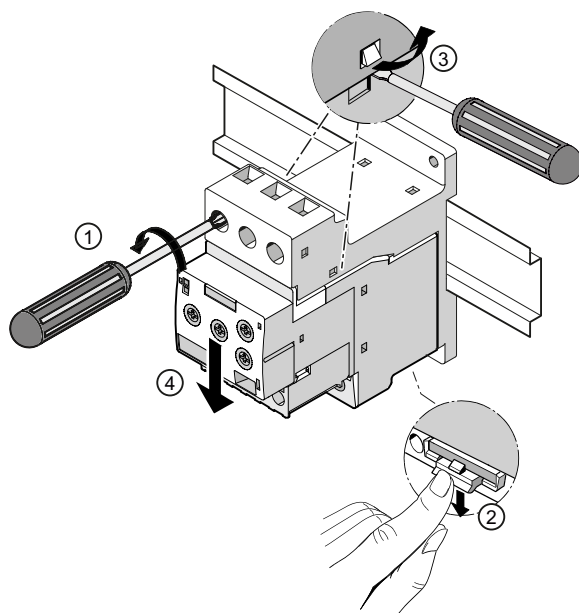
Montage Anschlussträger (Schraubanschlusstechnik im Hauptstromkreis)
